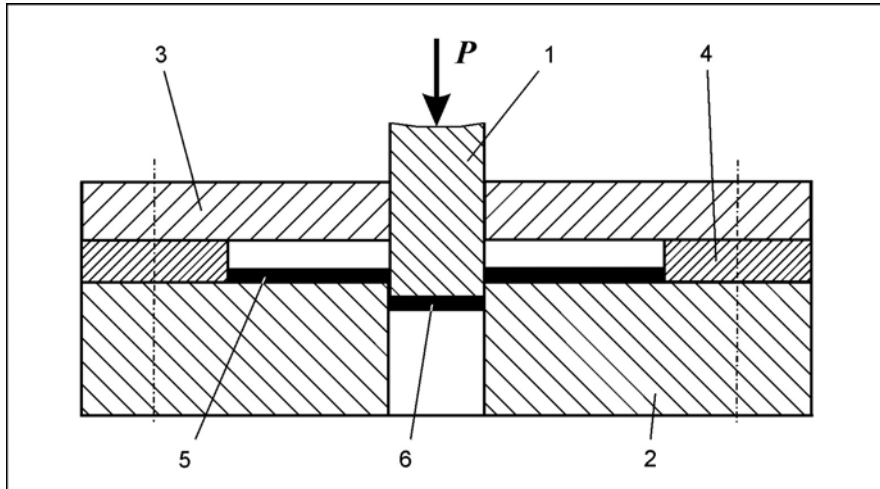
Схема операції пробивання: 1 – пробивний пуансон; 2 – пробивна матриця; 3 – жорсткий знімач; 4 – упор (графарет); 5 – заготовка, що пробивається; 6 – відхід від пробивання
